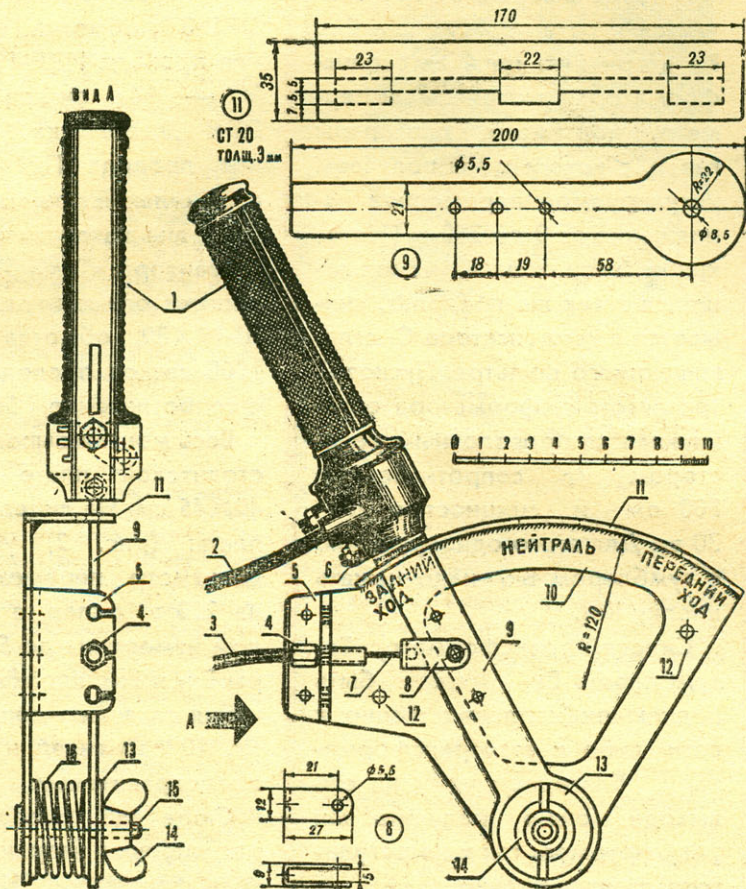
Комбинированный рычаг управления газом и реверсом:
